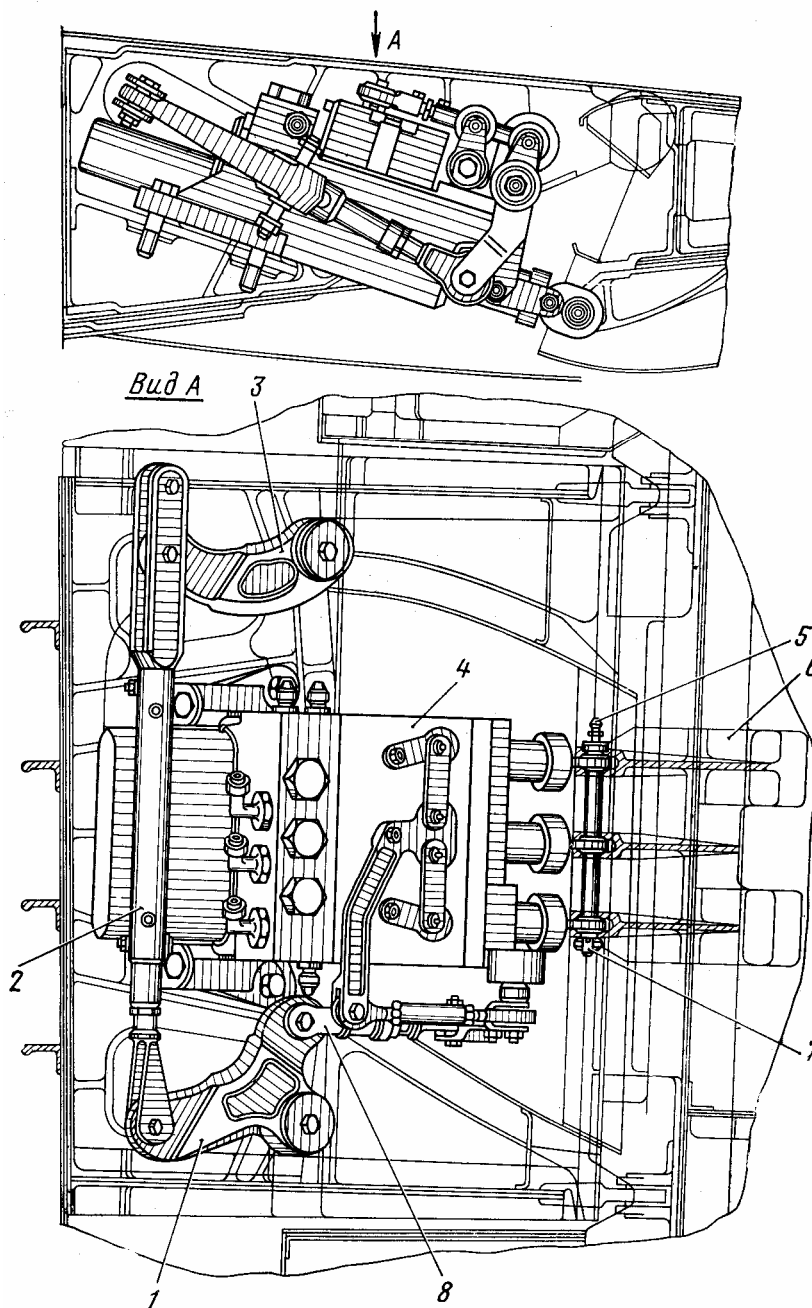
Установка рулевого привода РП-55 (на левом крыле):
